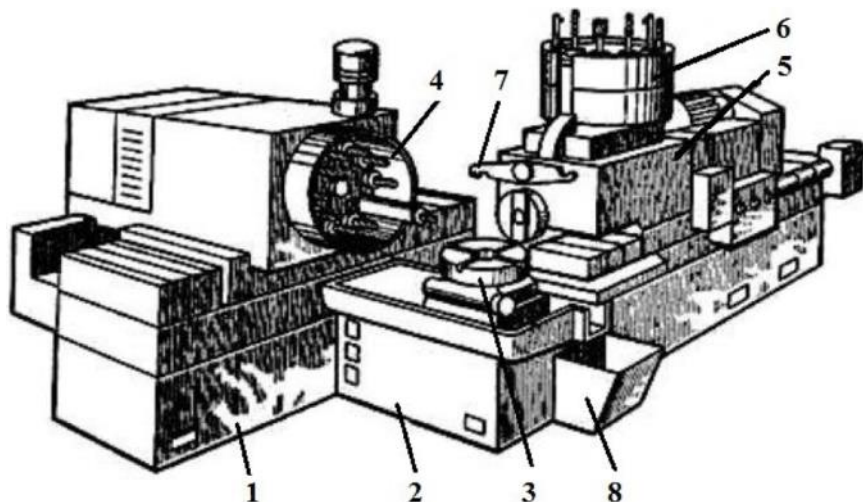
Схема агрегатного верстата з ЧПК.
